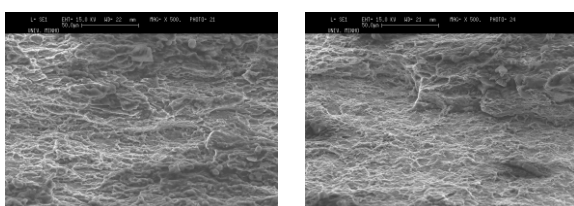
Imagens MEV das superfícies de fractura (6111-T4) - 500x
